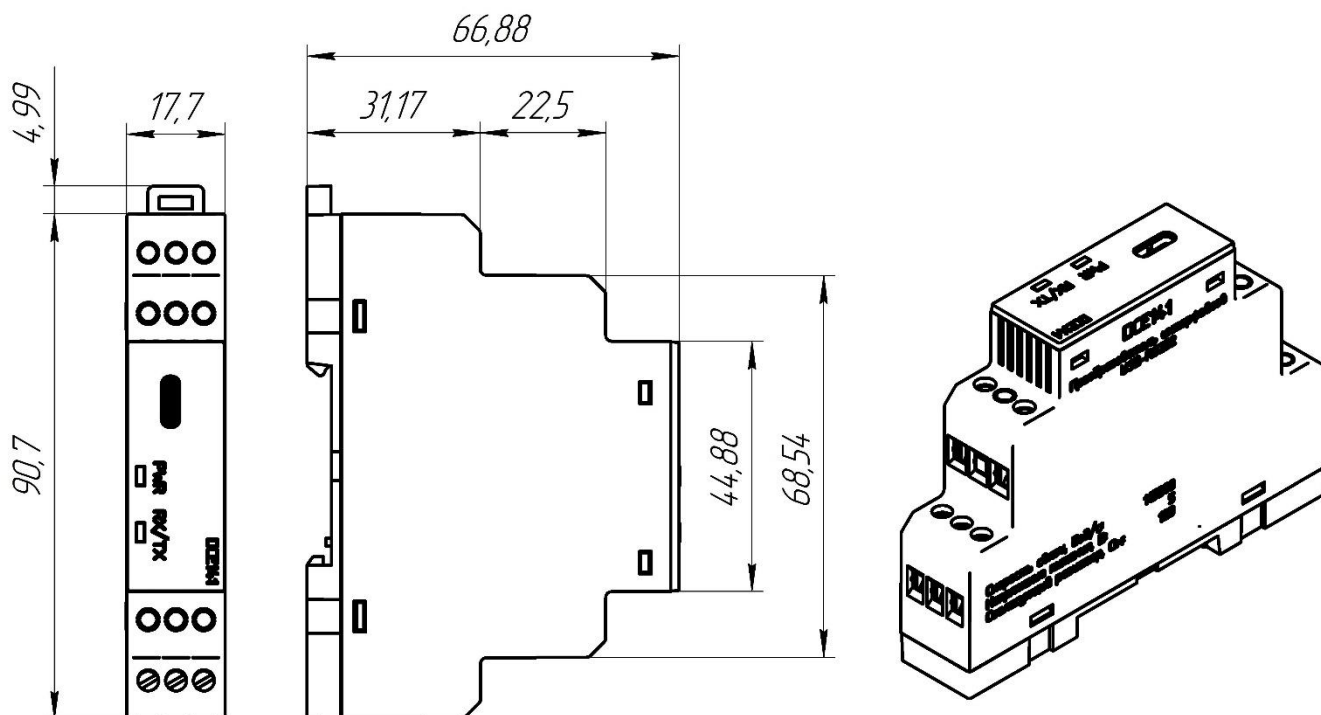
Габаритные размеры корпуса преобразователя интерфейсов USB-RS232 DCE141
